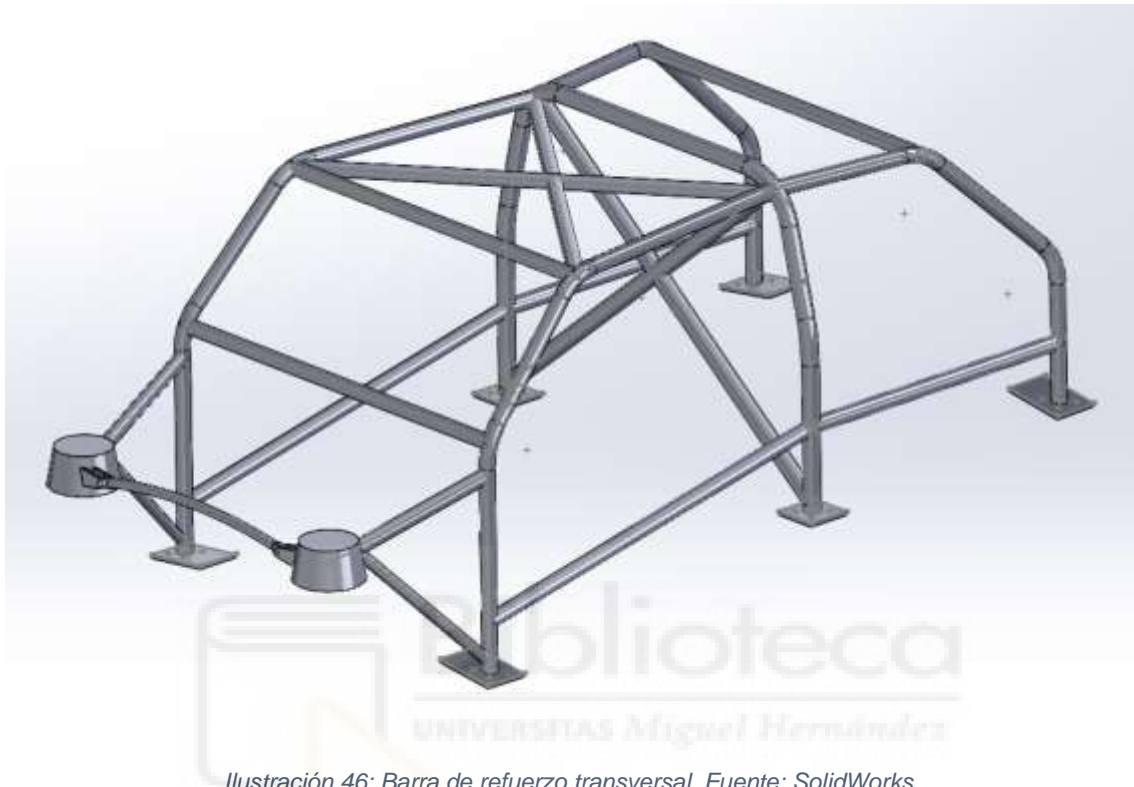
Barra de refuerzo transversal. Fuente: SolidWorks.
